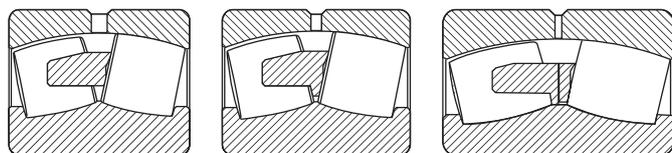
Geteilter, gefräster, innenringgeführter Messing-Fingerkäfig.
